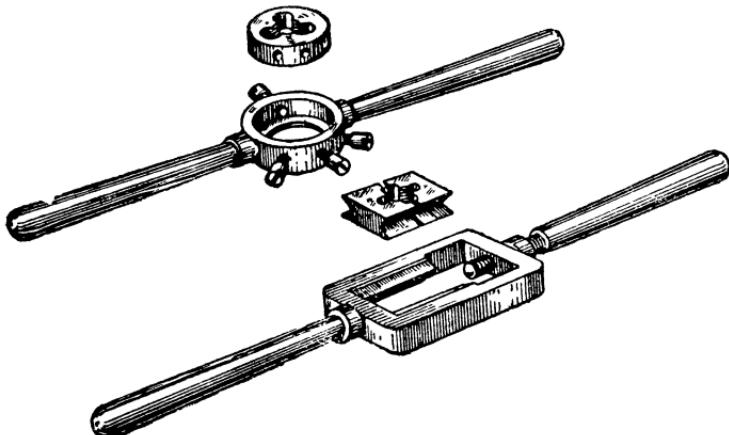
Лерка и леркодержатель, плашка и плашкодержатель.
